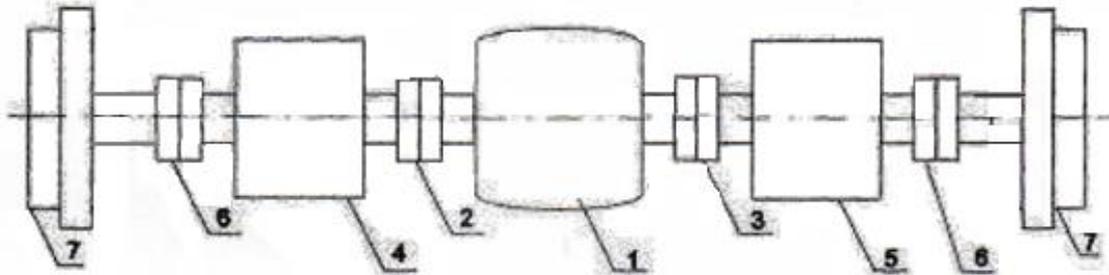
Конструктивная схема привода передвижения транспортного реечного устройства
